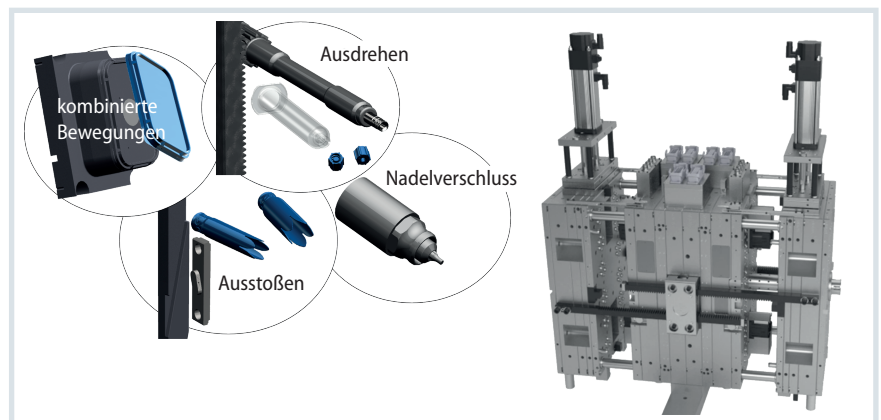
Lösungen für elektrische Werkzeugbewegungen, hier am Beispiel eines 72+72-fach Etagenwerkzeugs für die Verschlusskonus-Produktion © Schöttli/Husky
